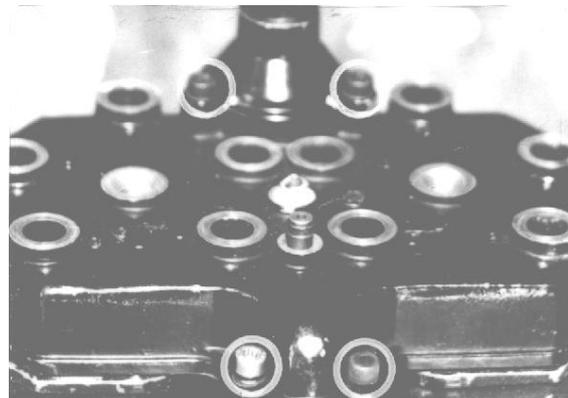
Flansch am Zylinderkopf / Thermostatgehäuse
